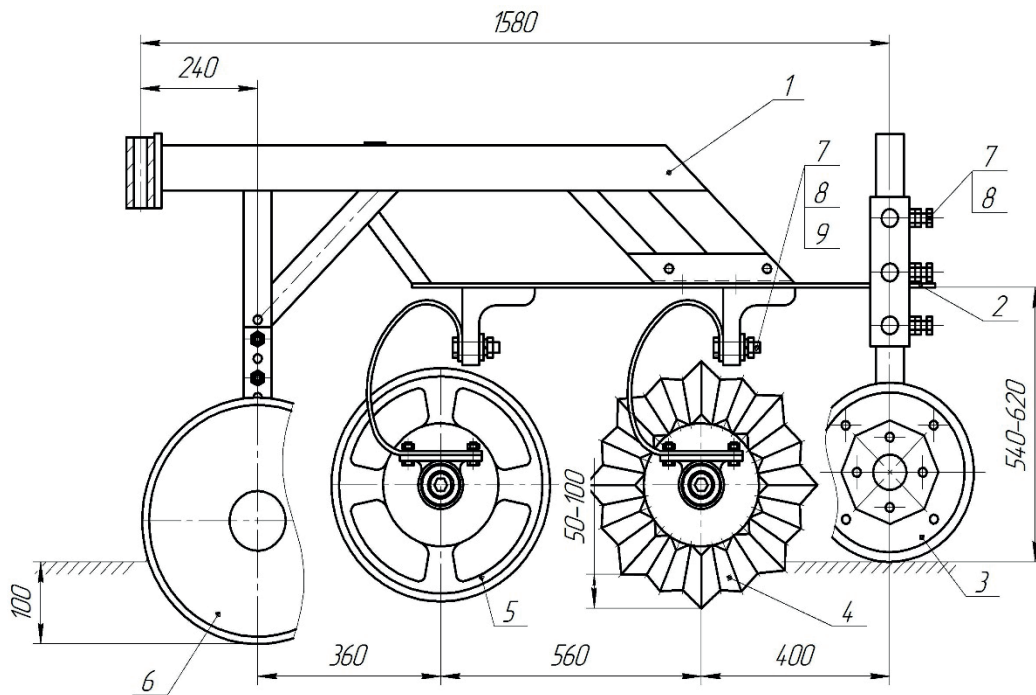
Конструктивна схема культиватора для роботи по агрофону: рослинні рештки
